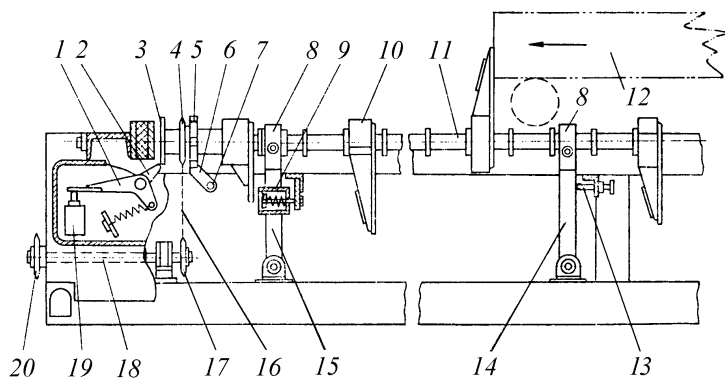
Устройство для отмера длин установки АЦ-1
